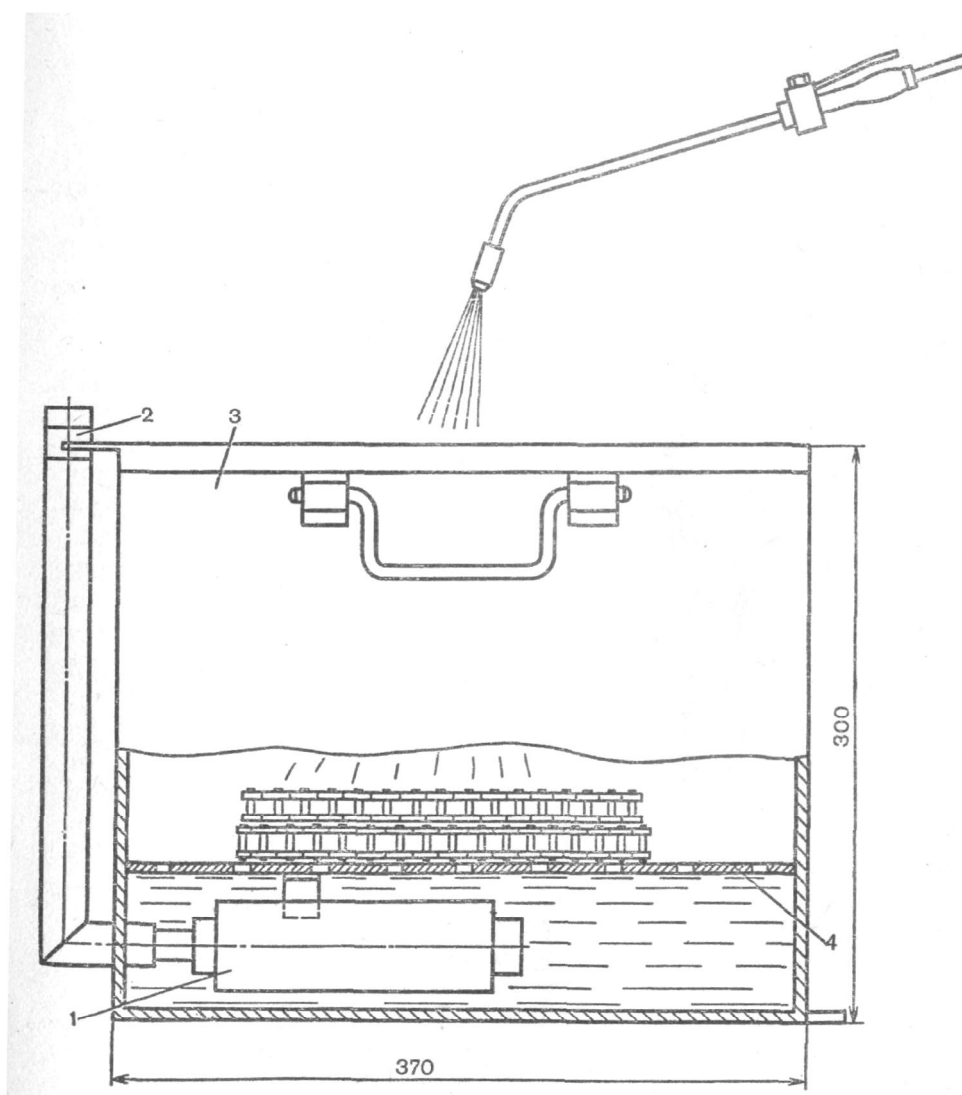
Ванна для промывки втулочно-роликовых цепей:
